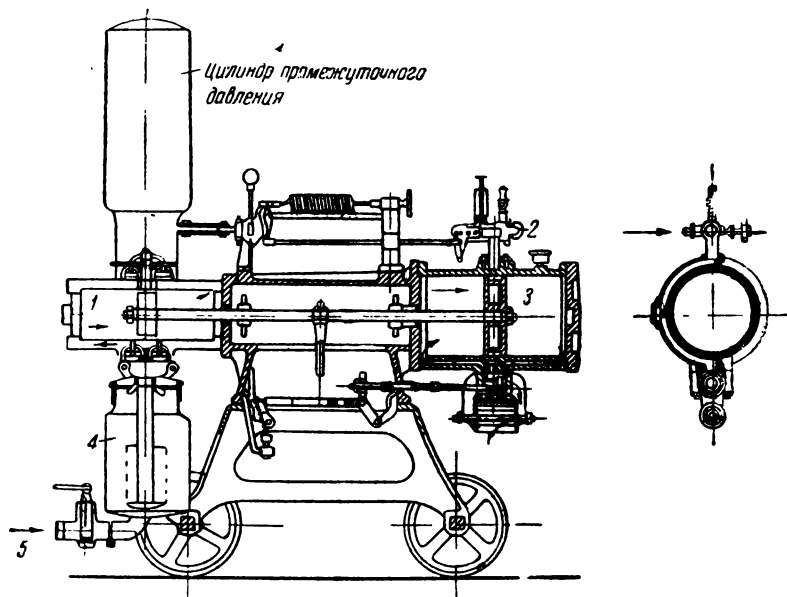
Регулятор давления, приводимый в действие сжатым воздухом: 1—насос; 2—впуск воздуха; 3—воздушный цилиндр; 4—всасывающий цилиндр; 5—впуск пива
